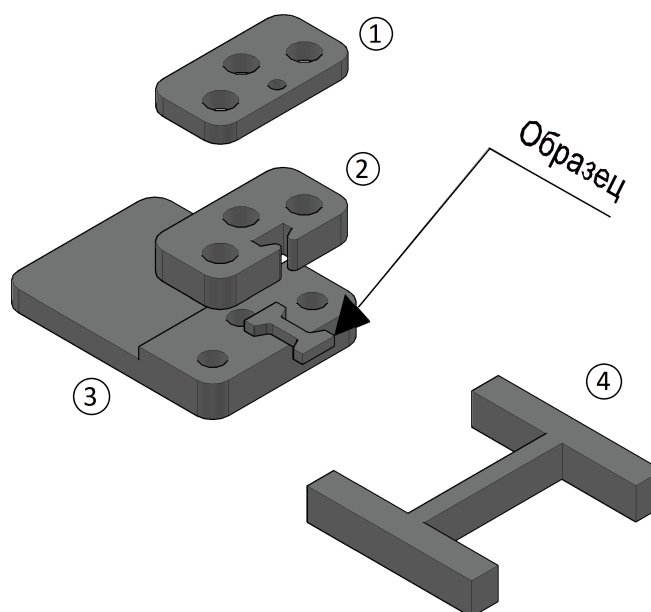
Схематичное изображение оригинальных захватов, использованных для статических и усталостных испытаний сплава ВТ6: 1) Прижимная пластина; 2) Губка; 3) Базовая плита; 4) Фиксирующая скоба
